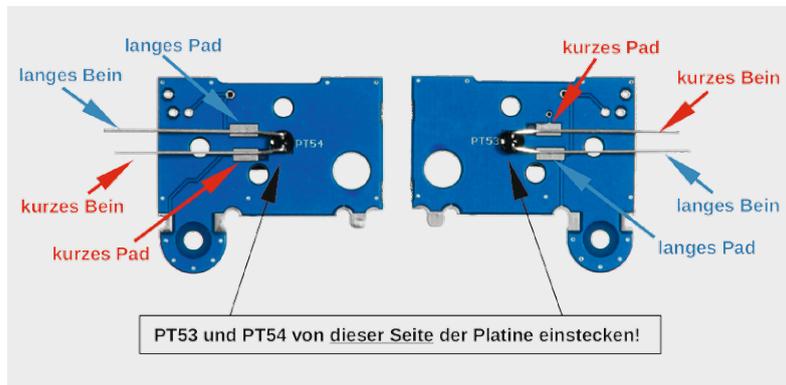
Detaillierter geht es kaum – die Bauanleitung lässt keine Frage offen.
